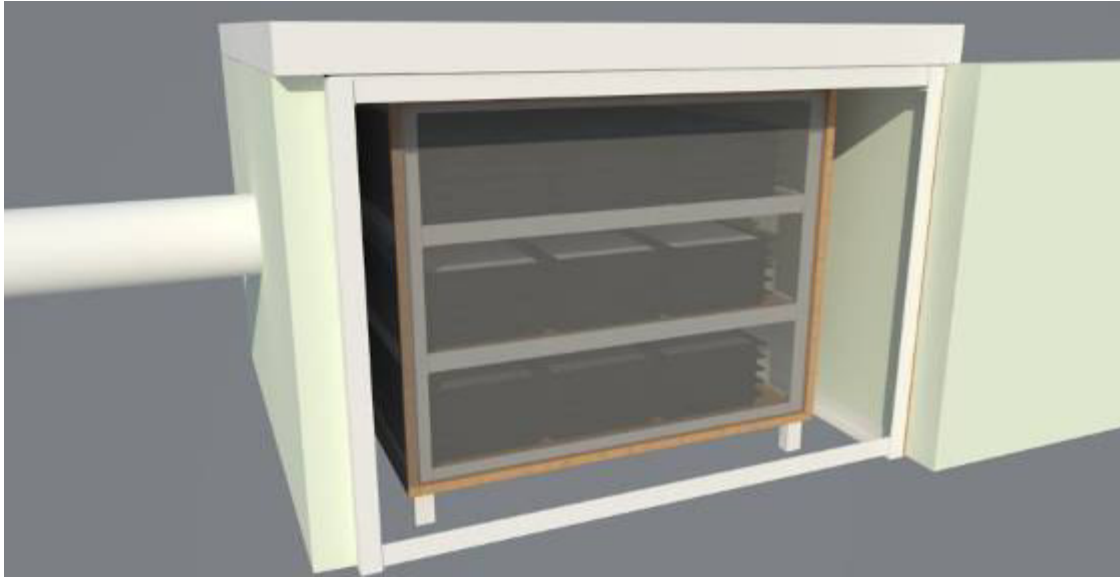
Перший варіант конструкції камери для теплової обробки нагрітим повітрям бетонних тротуарних плиток
